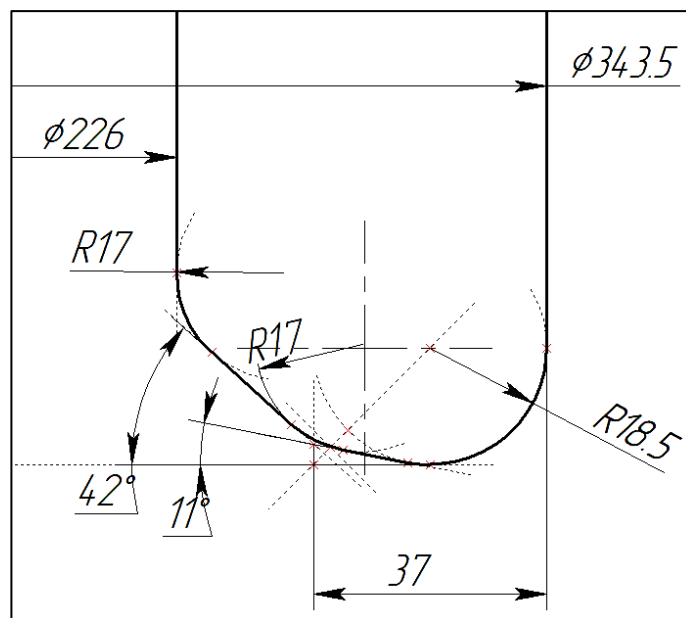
Рабочая кромка совмещенного инструмента для изготовления бака автоклава
